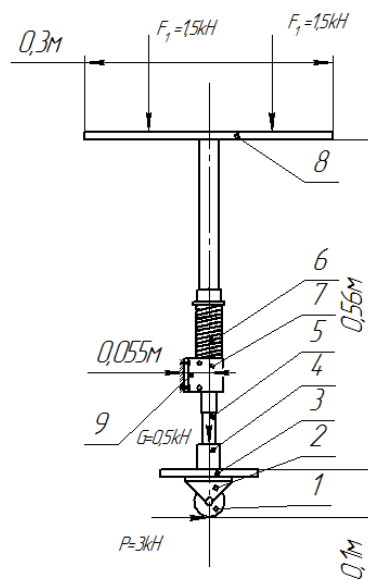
Схема підвісного обладнання лабораторного стенда МЗР
